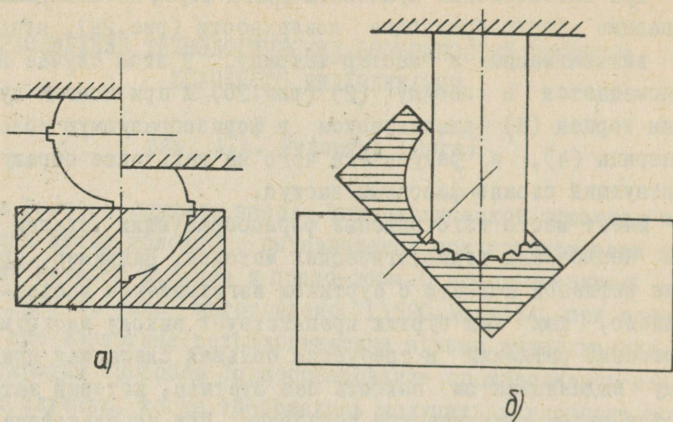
Схема выдавливания формообразующей поверхности с элементами поднутрений.
